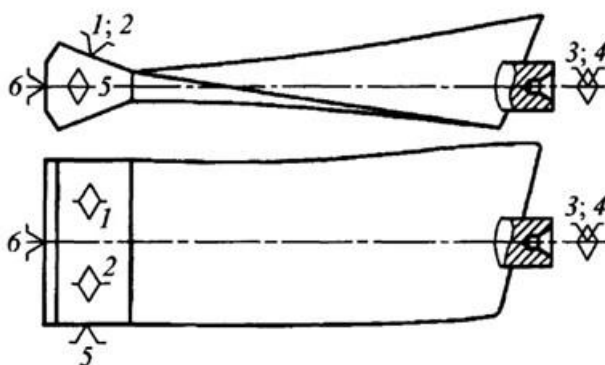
схема базування заготовки з хвостовиком типу ластівчин хвіст при фрезеруванні проточної частини.
